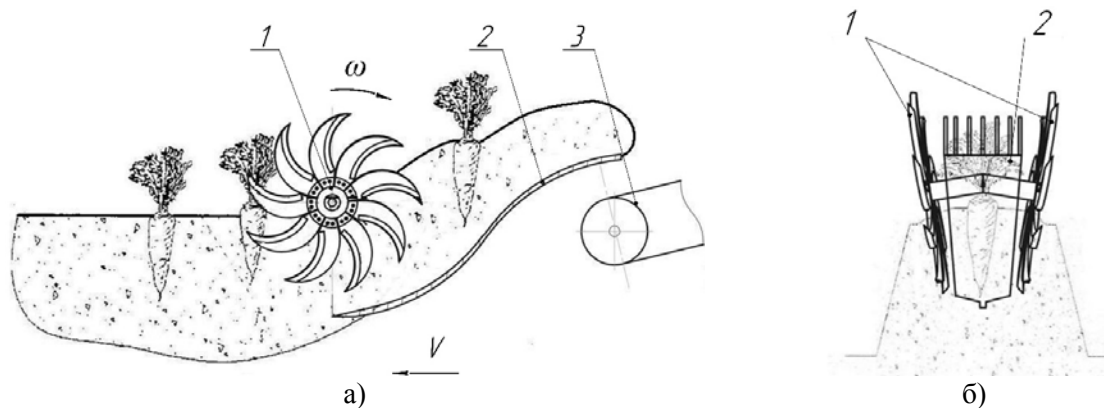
Схема загального вигляду викопуючого робочого органа з супутнім фрезеруванням:
